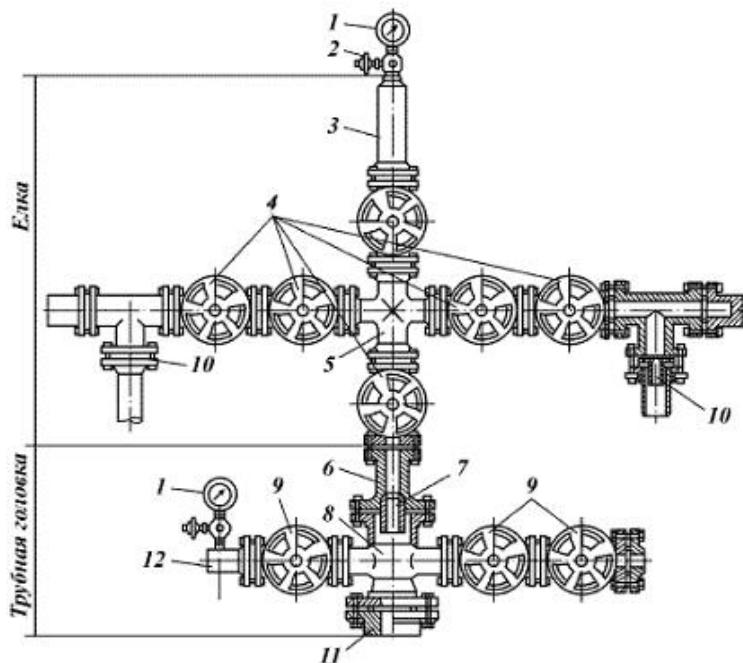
Арматура фонтанная крестовая для однорядного подъемника:
